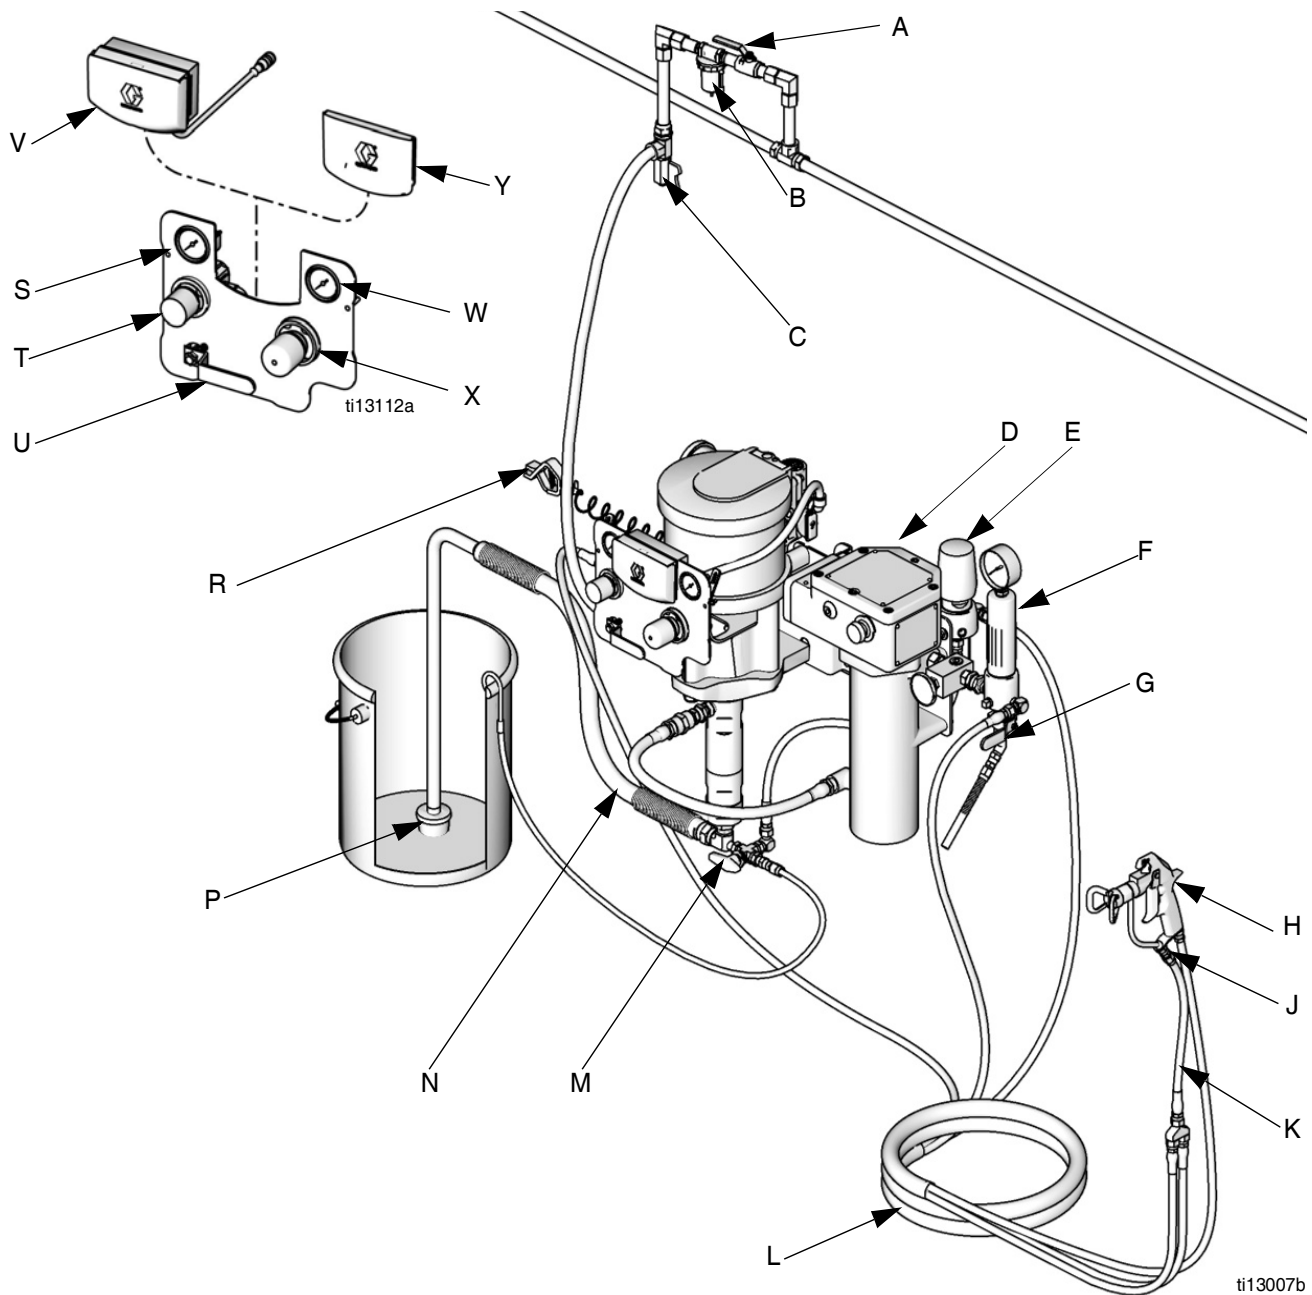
Installazione tipica (il pacchetto potrebbe non includere tutti gli elementi illustrati)
